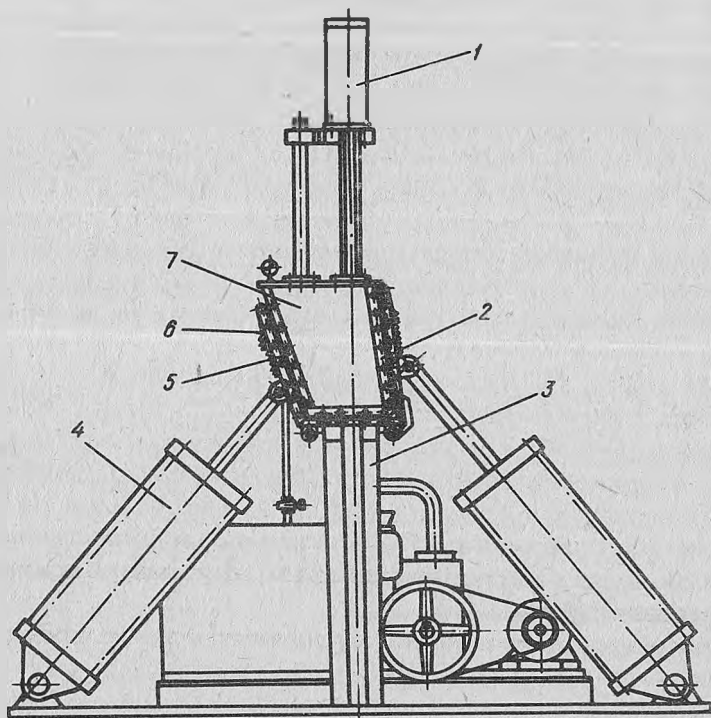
Вакуумный пресс для изготовления из шпона гнуктоклеевых блоков глубокого профиля:
